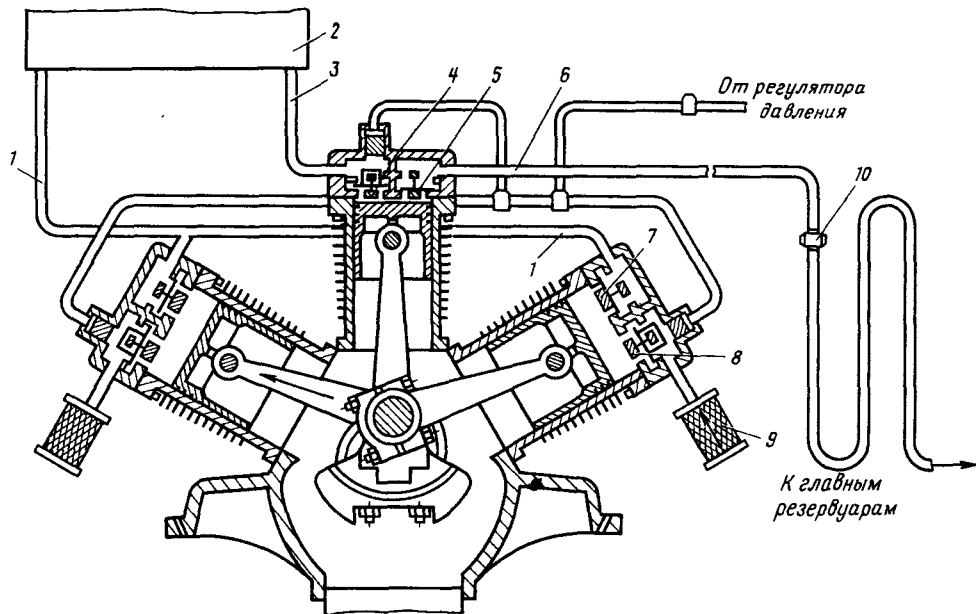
Схема работы компрессора типа К2-Лок-1:
